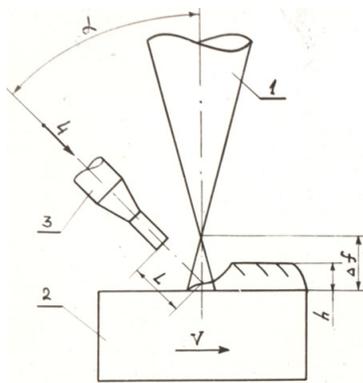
Схема газопорошковой лазерной наплавки: α - угол наклона сопла к оси лазерного луча, V - скорость перемещения образца, L - расстояние сопла до поверхности образца, Δf - степень расфокусировки, h - высота наплавленного валика, 1 - луч лазера, 2 - образец, 3 - сопло, 4 - подача порошка.
